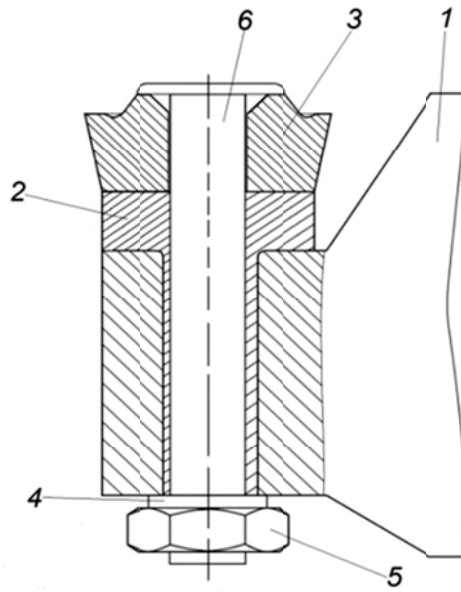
Исследуемая конструкция сборного чашечного резца
